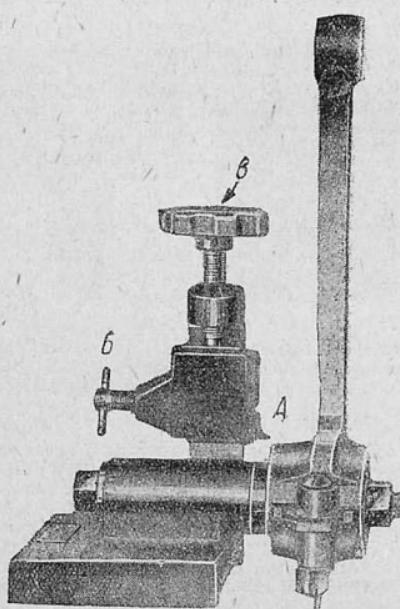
Приспособление по обработке галтелей на торцах шатунного подшипника
